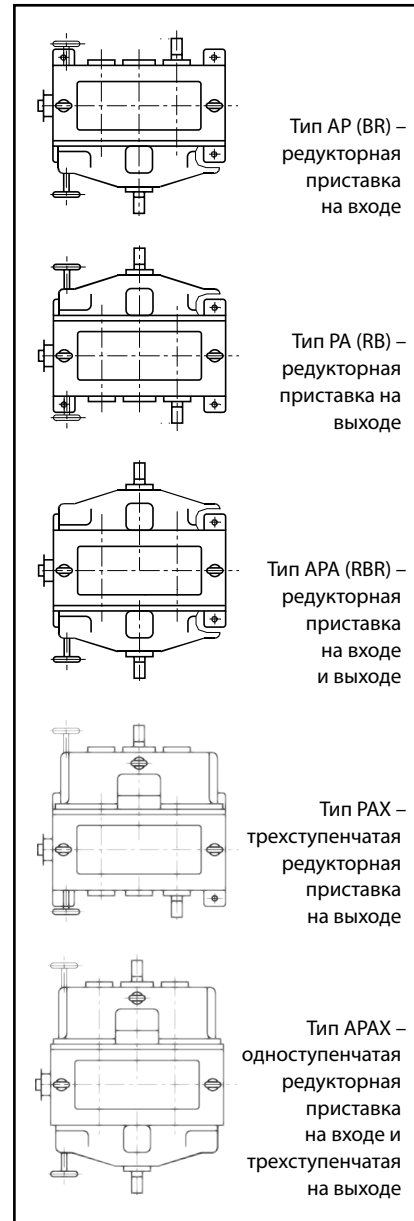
Комбинированные конструкции вариаторов с редукторными приставками
